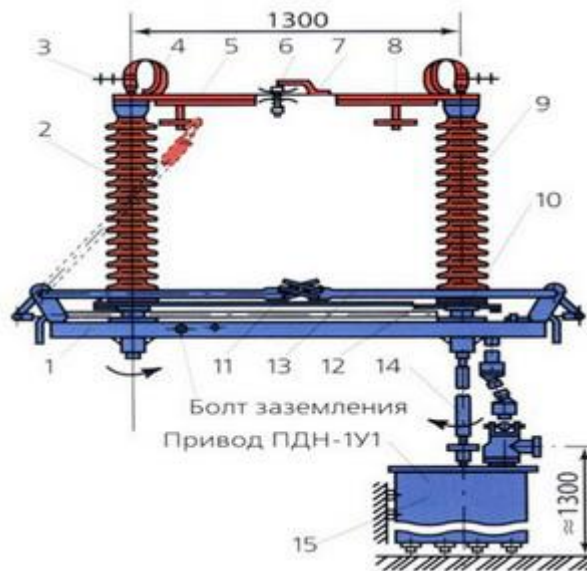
Внешний вид разъединителя РНДЗ-110
